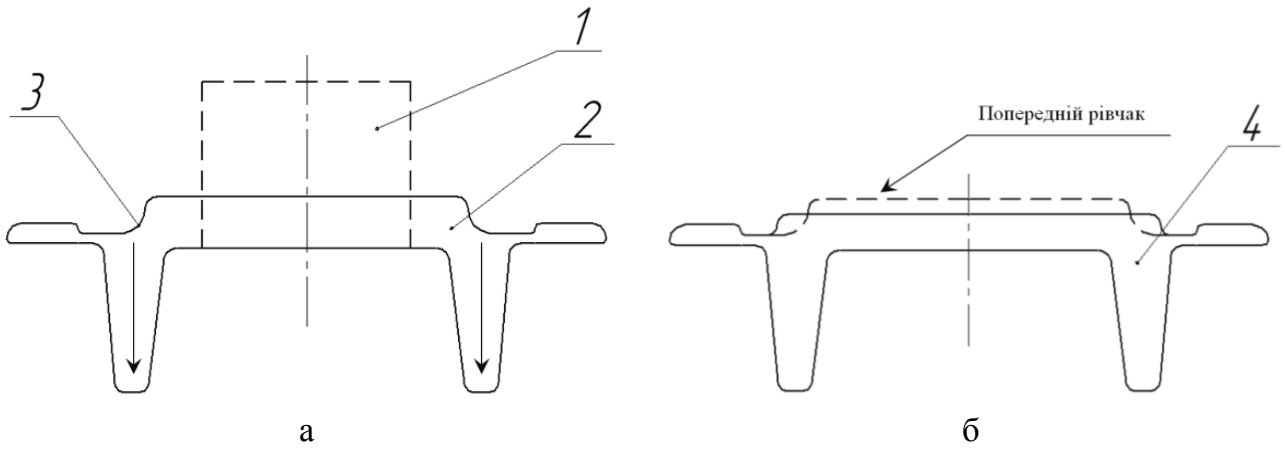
Попередній (а) і остаточний (б) ривчак штампа: 1 - заготовка з прокату або кований злиток; 2 – поковка; 3 - порожнини в тілі поковки; 4 - готова поковка
